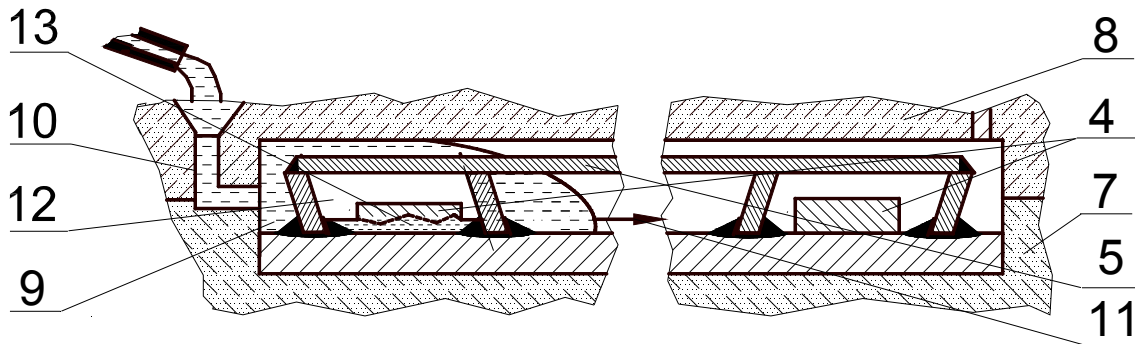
Форма з встановленою в неї збірною робочою пластинною для заливання металом основи.
